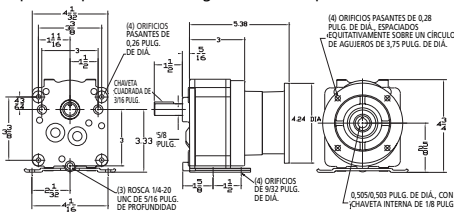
Dimensiones - 1L511-1L516 y 1L537
